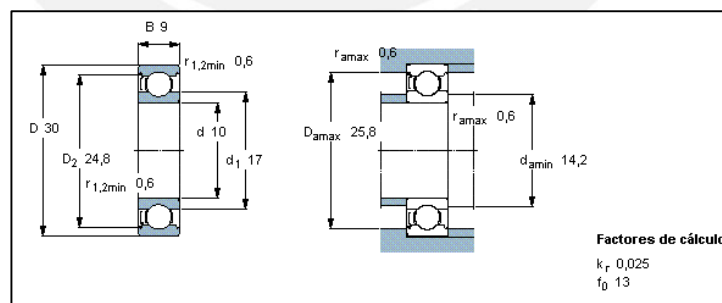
Dimensiones del rodamiento de las juntas.
